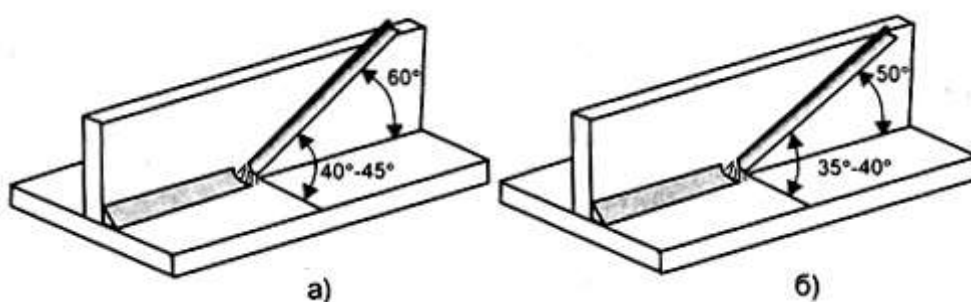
Сварка таврового соединения в нижнем положении.
